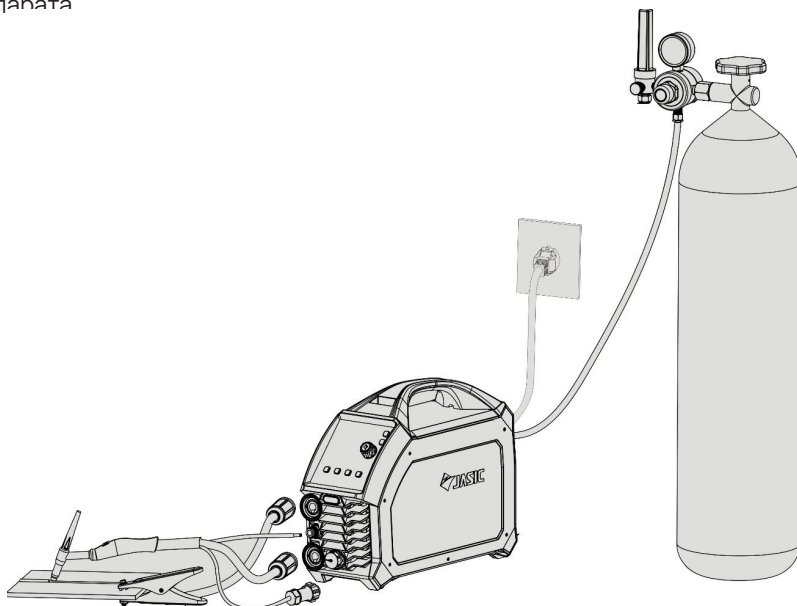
Подключение сварочной горелки, кабеля заземления и газового баллона
